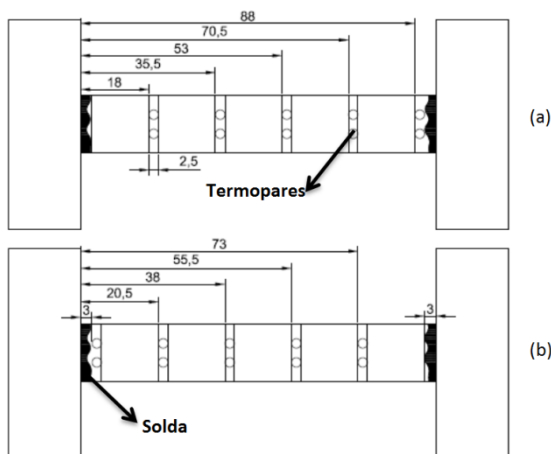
Defasagem dos conjuntos fluxímetro de calor e placa de cobre.
